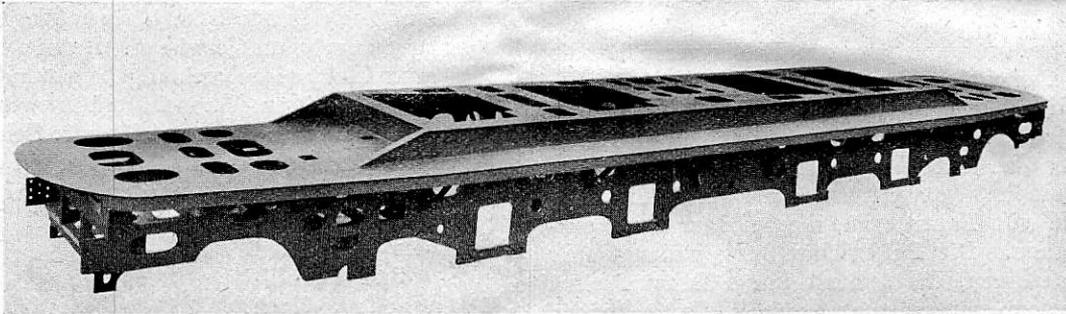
Geschweißter Rahmen für 1' Do 1'-Lokomotive.
